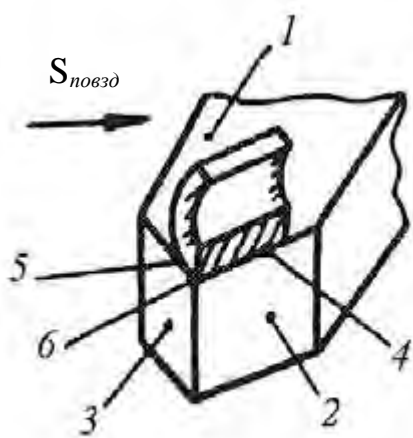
Поверхні й інші елементи різальної частини інструменту
